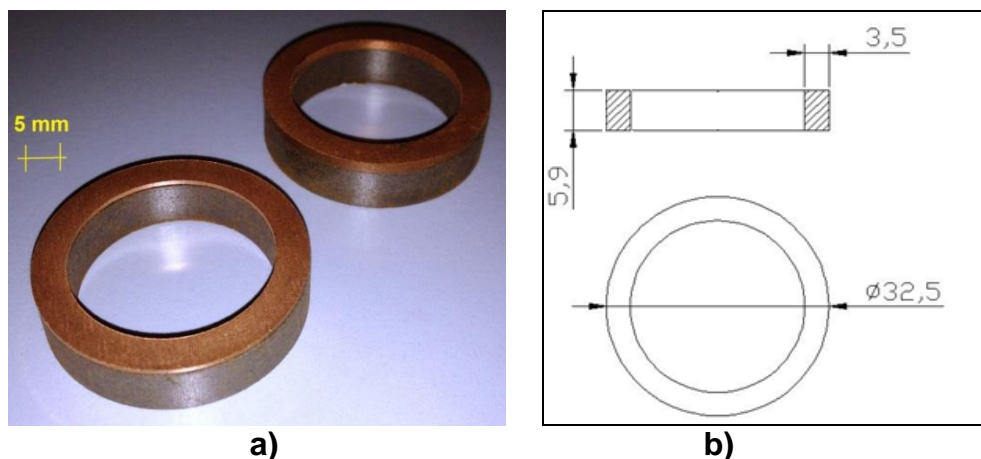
a) Desenho técnico, vista frontal em corte e superior do inserto, dimensões em mm. b) Insertos com anéis de cobre por cima, como foram colocados no forno para sinterização em dois corpos.
